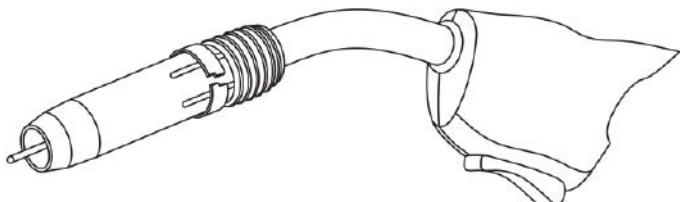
Порядок заправки сварочной проволоки.
